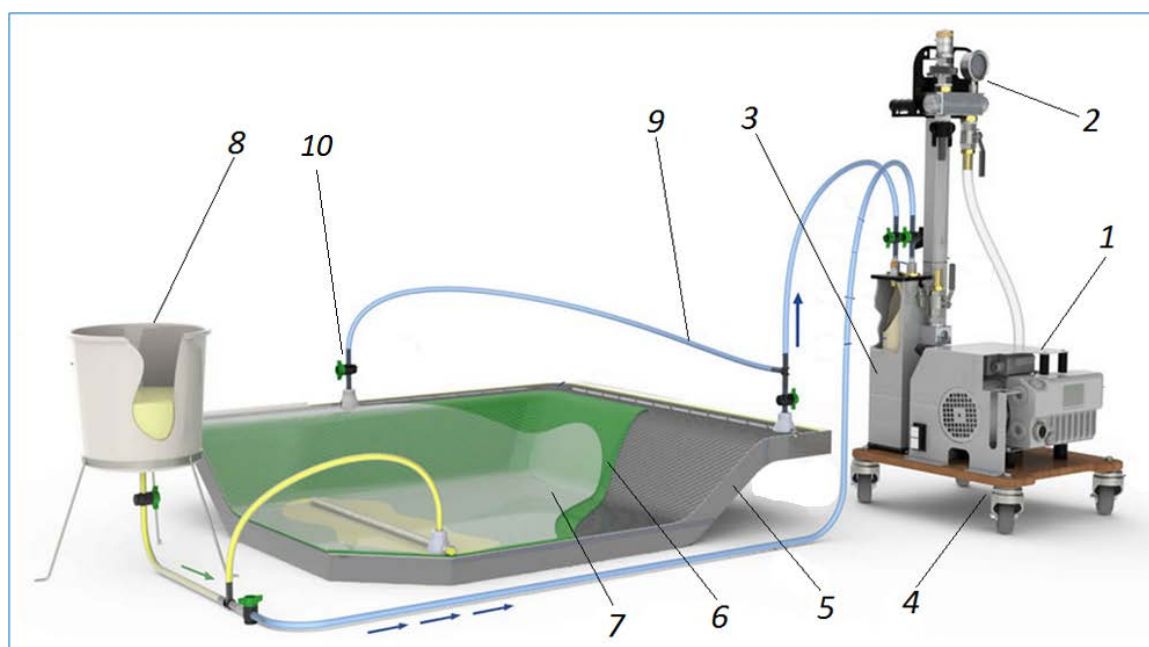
Instalație de formare prin transferul rășinii în vid :
